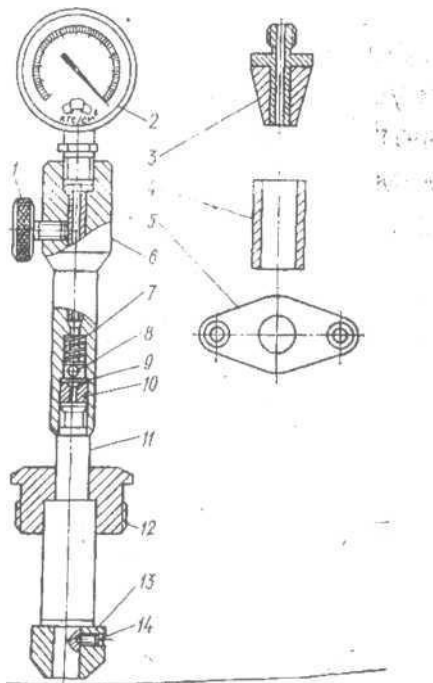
Компресиметр КИ-861: 1— вентиль; 2 — манометр; 3, 13 — наконечники; 4 — втулка; 5 — фланець; 6 — корпус; 7 — пружина; 8 — кульковий клапан; 9 — гумова прокладка; 10 — регулювальний гвинт; 11— трубка; 12 — з'єднувальна муфта; 14 — установочний гвинт.
